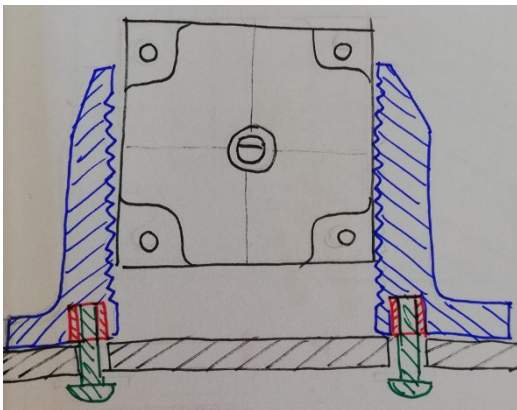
Skizze des Befestigungsmechanismus für den Motor
